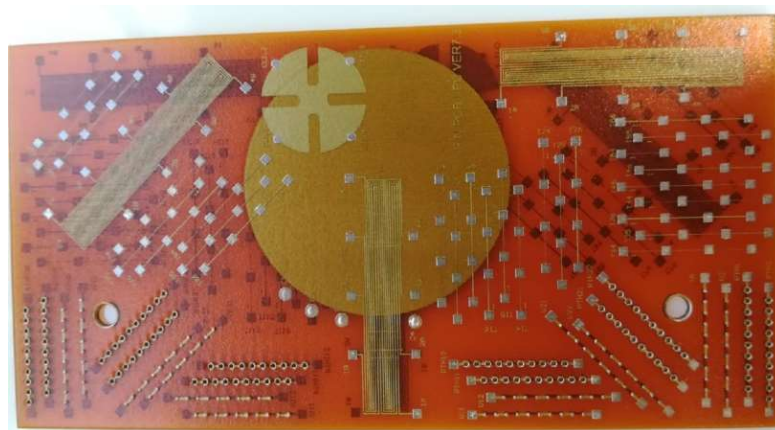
Печатная плата, изготовленная с помощью 3D-принтера DragonFly
